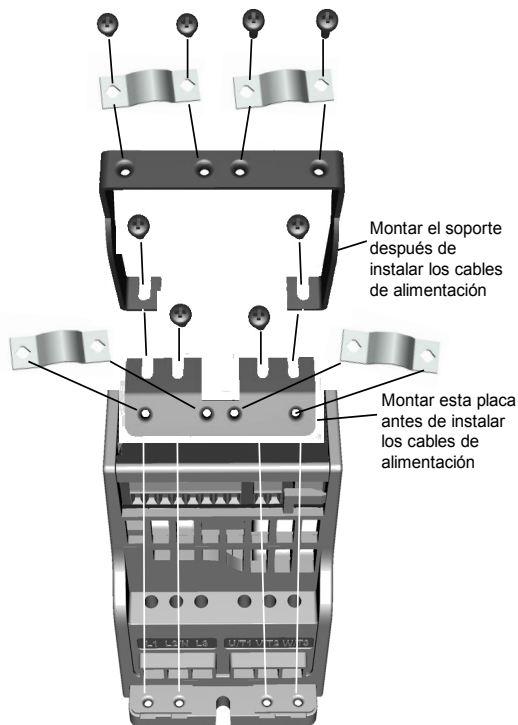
Montaje de la placa PE y del soporte de cables API, MI1 - MI3
